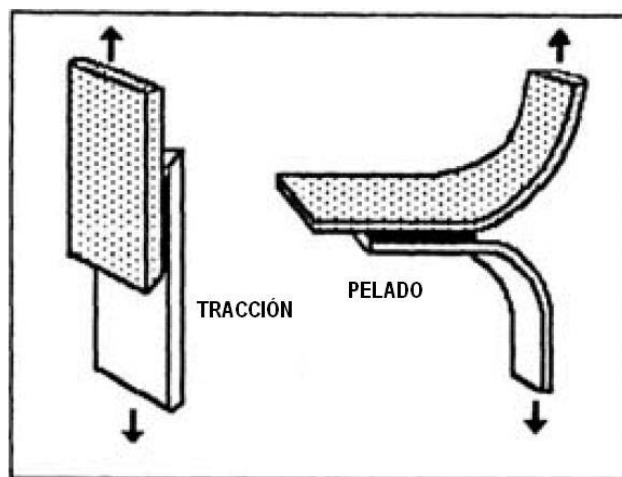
Esquema de los ensayos de la resistencia de la soldadura por tracción y pelado (Rollin & Fayoux 2005).
